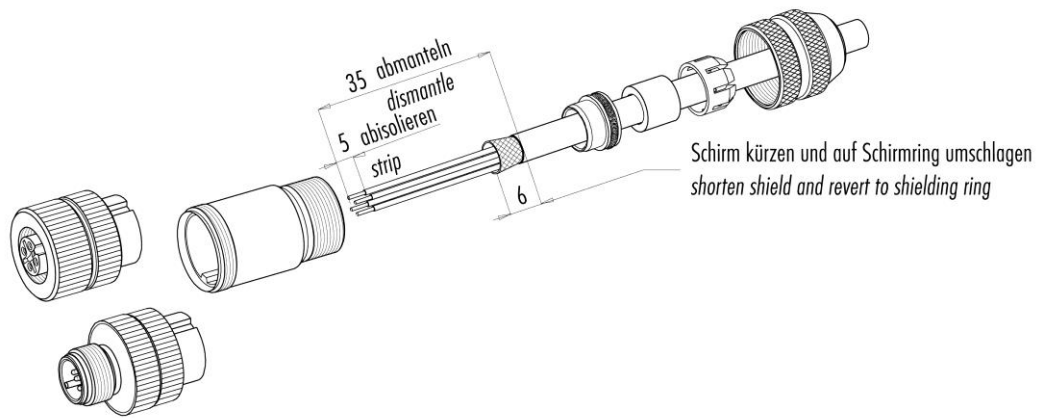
Montageanleitung für geschirmte Steckverbinder Anschlüsse 1, 2, 4 und 5
